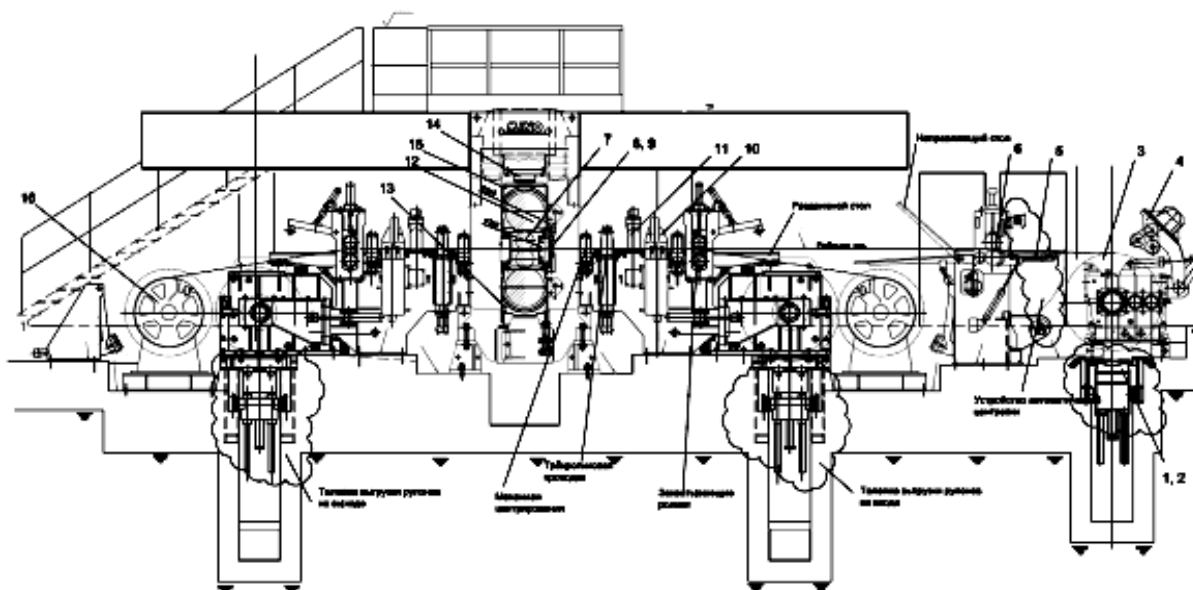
Одноклетьевой четырехвалковый реверсивный стан холодной прокатки 260/560x550 фирмы «MINO»
